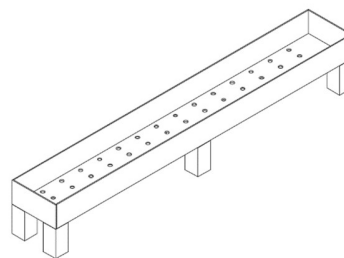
Diseño conceptual de las camas elevadas vista 3D.
